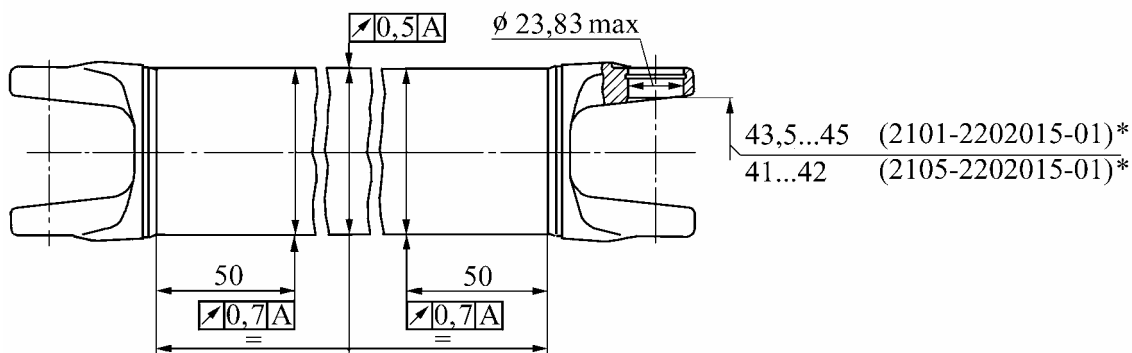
Вал карданный задний 2101/2105-2201015-01.
